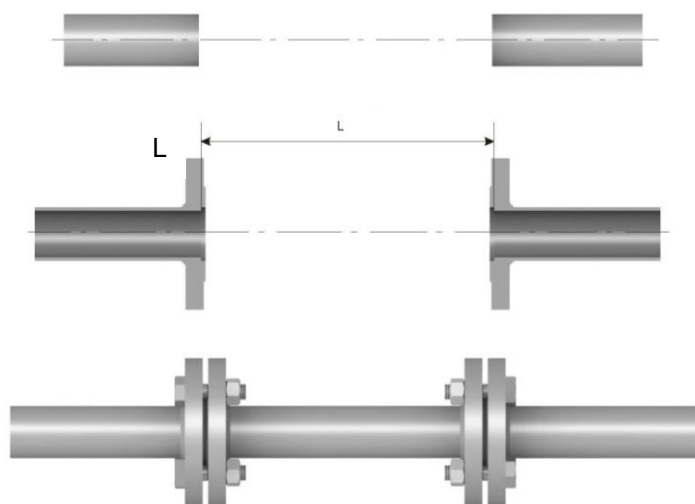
Подготовка трубопровода к монтажу счетчика-расходомера
